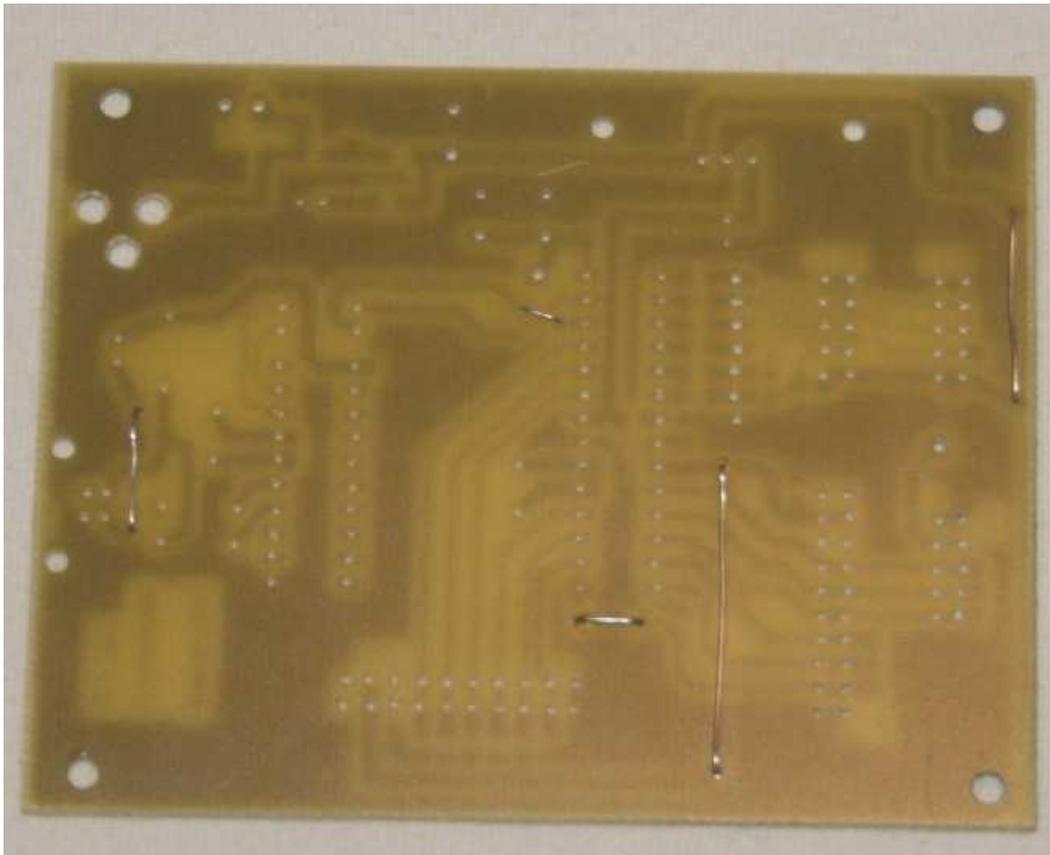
Platine mit Drahtbrücken und den Bohrungen für die PWR Buchse
